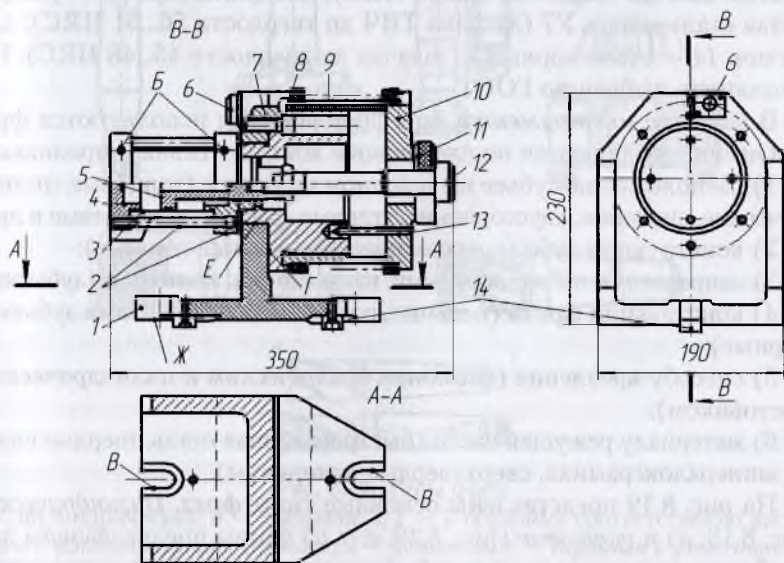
Многоместное приспособление с гидроприводом для фрезерования дисковой фрезой сквозных пазов на поршневых кольцах
